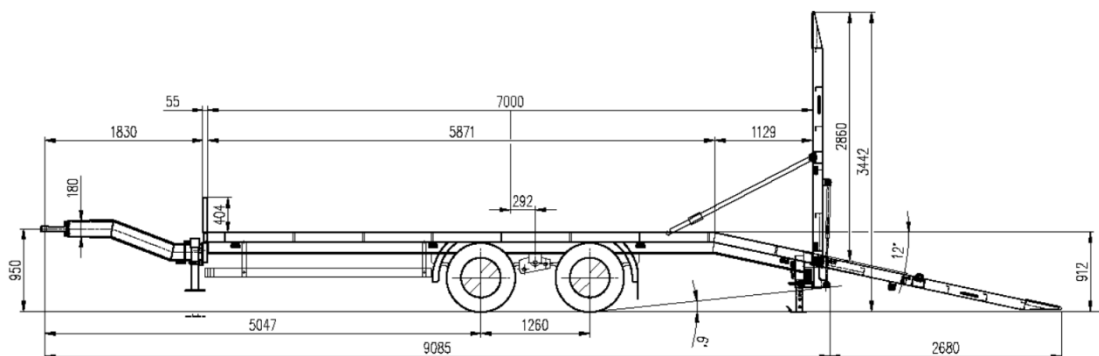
Přívěsový podvalník Goldhofer CHTP 11
